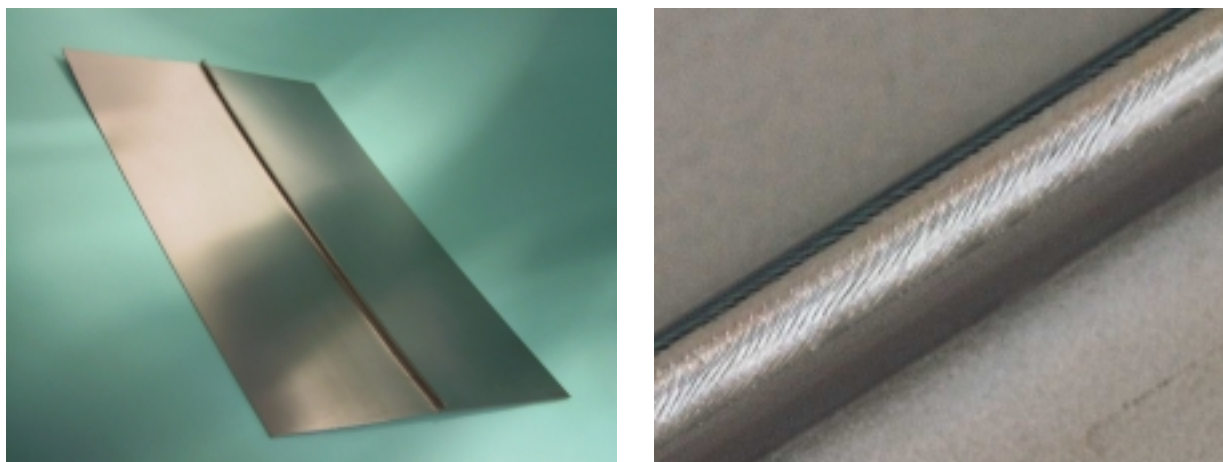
Junta em aresta Ti2, chapas soldadas para os ensaios (esquerda), detalhe dos flanges soldados (direita).
